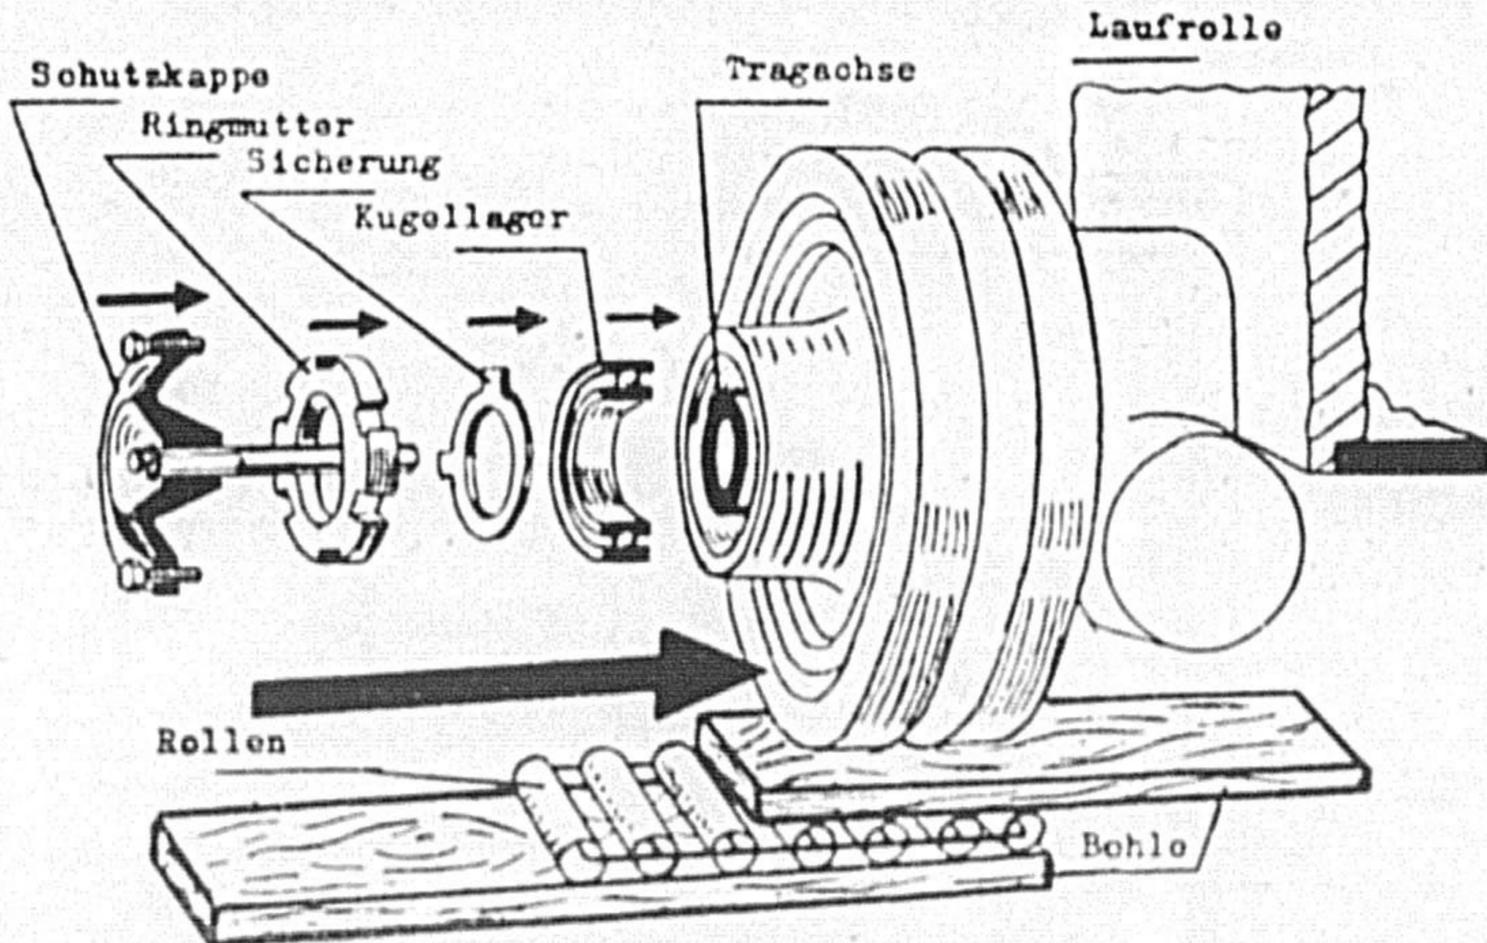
Einbau der ersten Laufrolle mit dem Rollschlitten Sk 10.006
